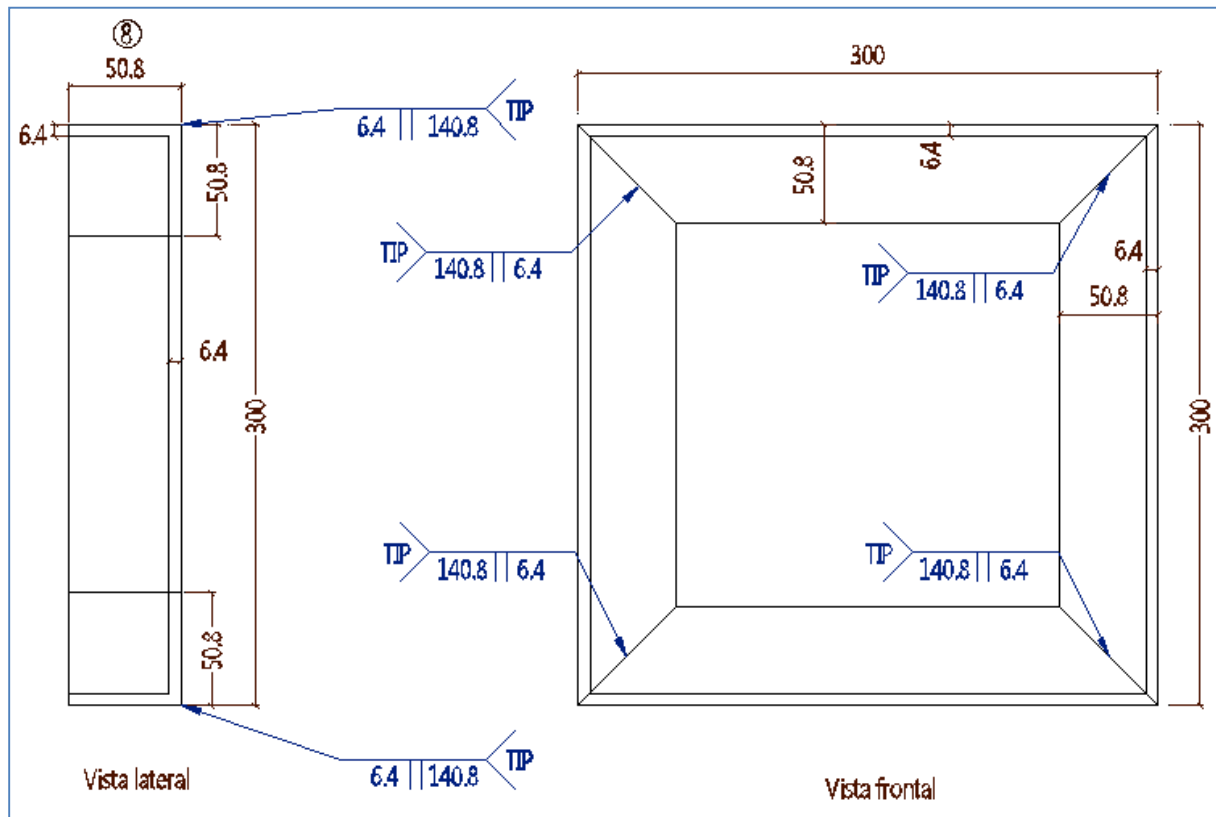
Detalle despiece pieza No.8 modelo 3 tensión.
